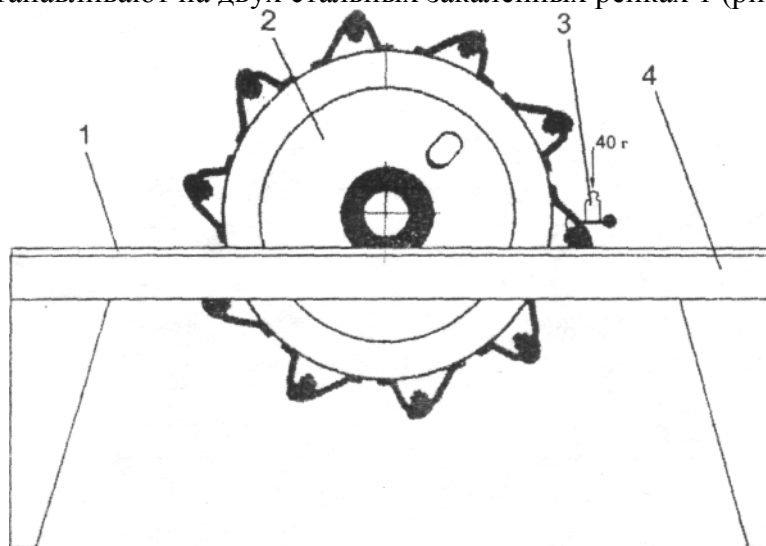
Схема приспособления для статической балансировки молотильного барабана:
